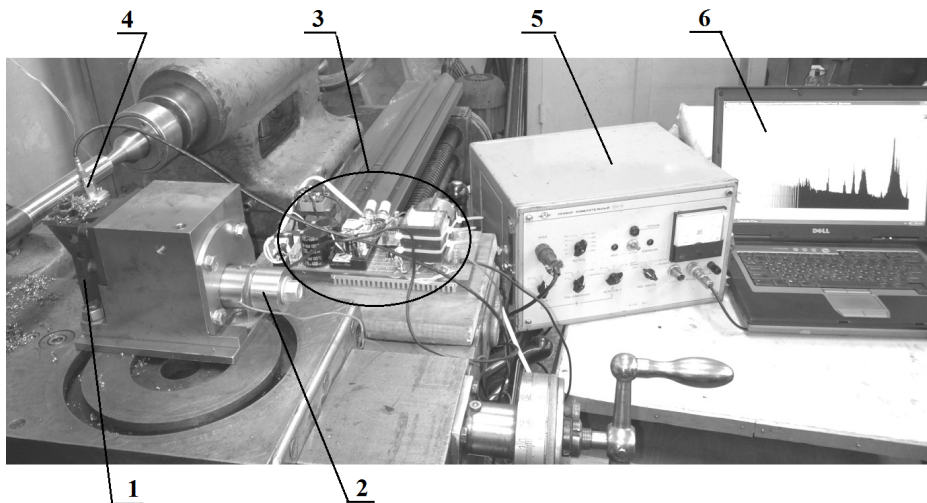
Загальний вигляд стенду на базі токарно-гвинторізного верстата:
